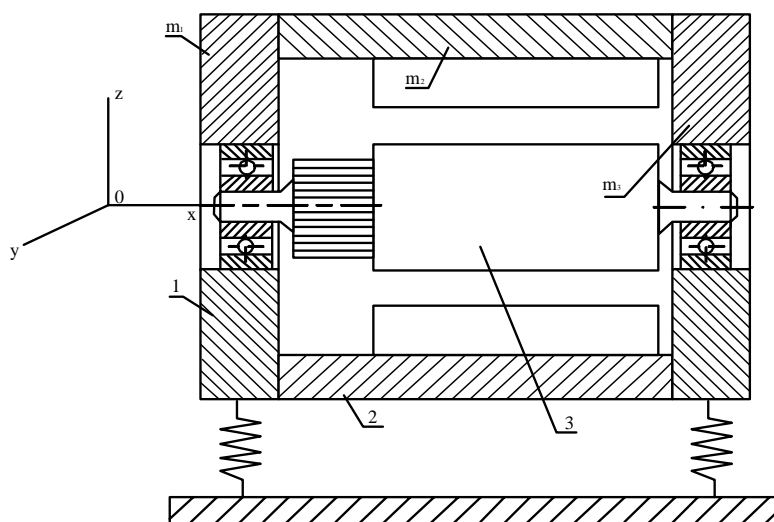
Простейшая схема тягового двигателя как упругой колебательной системы: 1 – подшипниковые щиты; 2 – станина с магнитом; 3 – жесткий ротор
